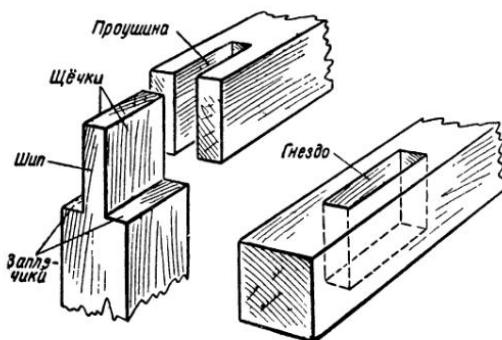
Шиповое соединение сквозным одинарным шипом с двумя заплечиками.
